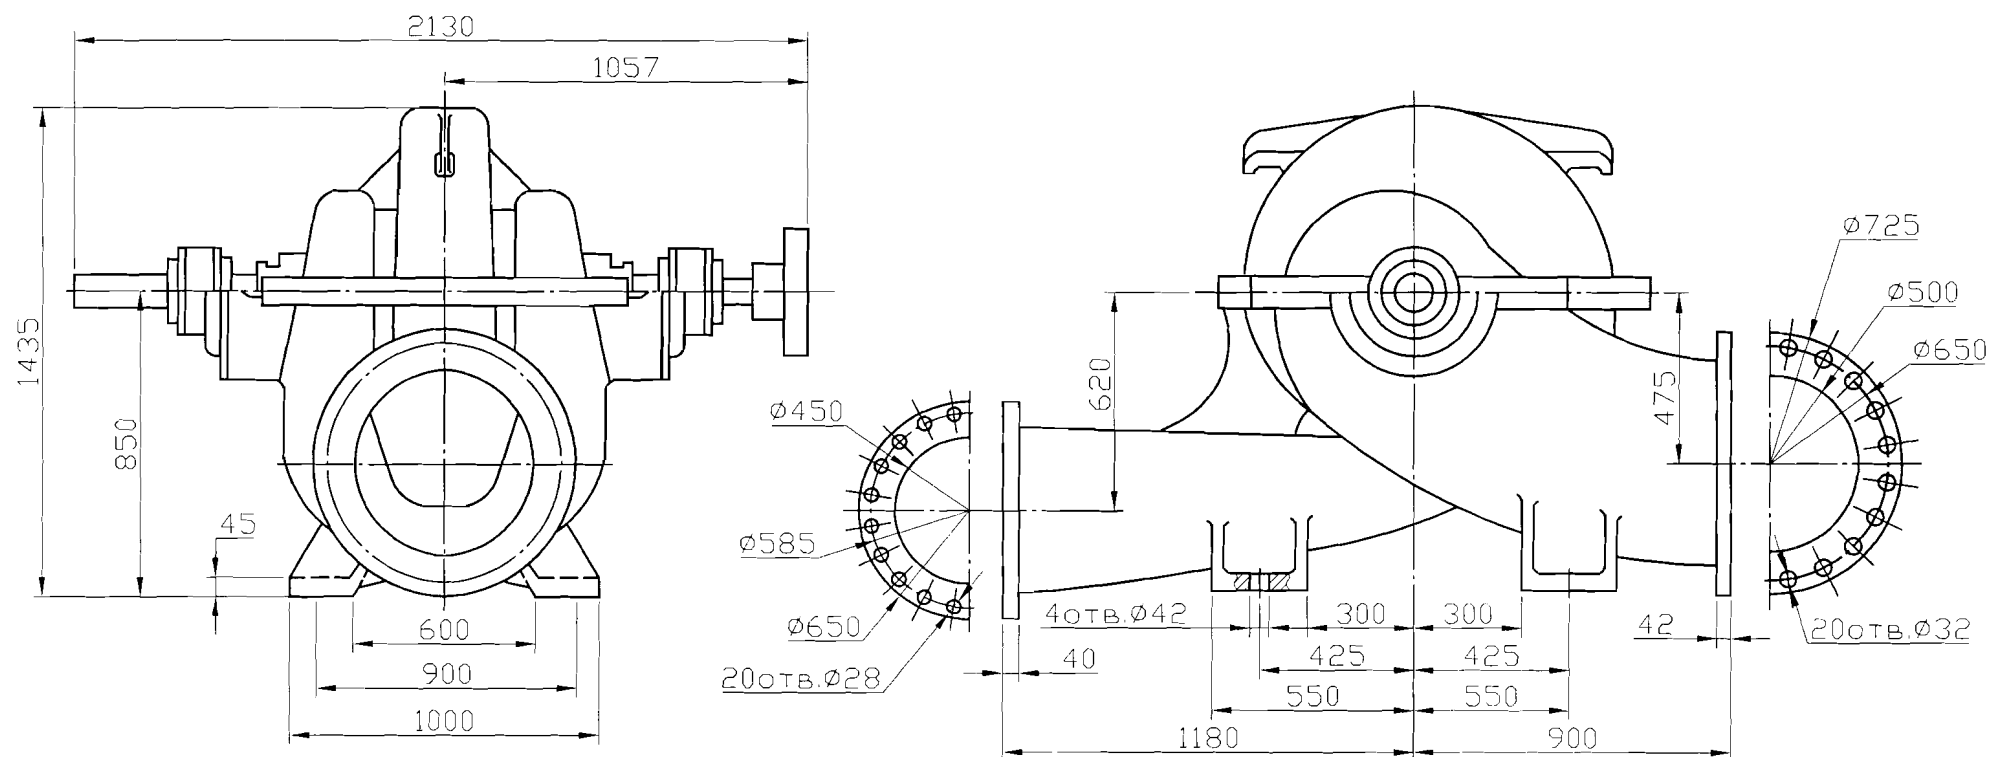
Габаритный чертеж насоса типа Д2500-62
